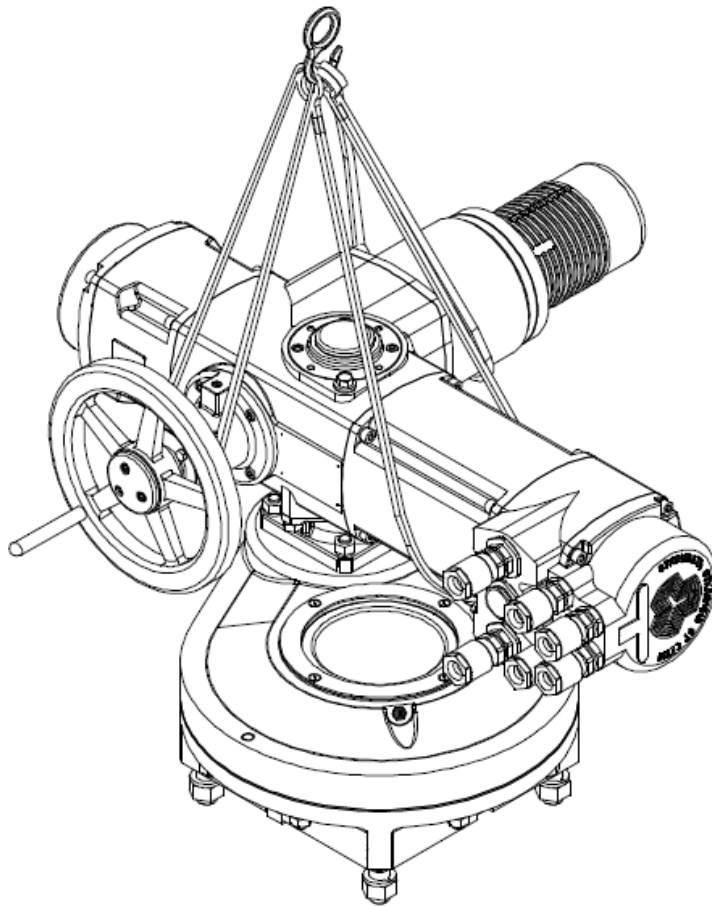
в – Схема строповки привода конструктивной схемы 410
